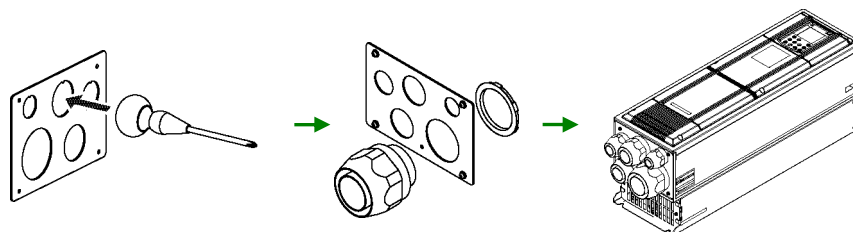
Apertura delle sezioni semi-perforate nella piastra di cablaggio e posizionamento dei pressacavi o delle canaline
